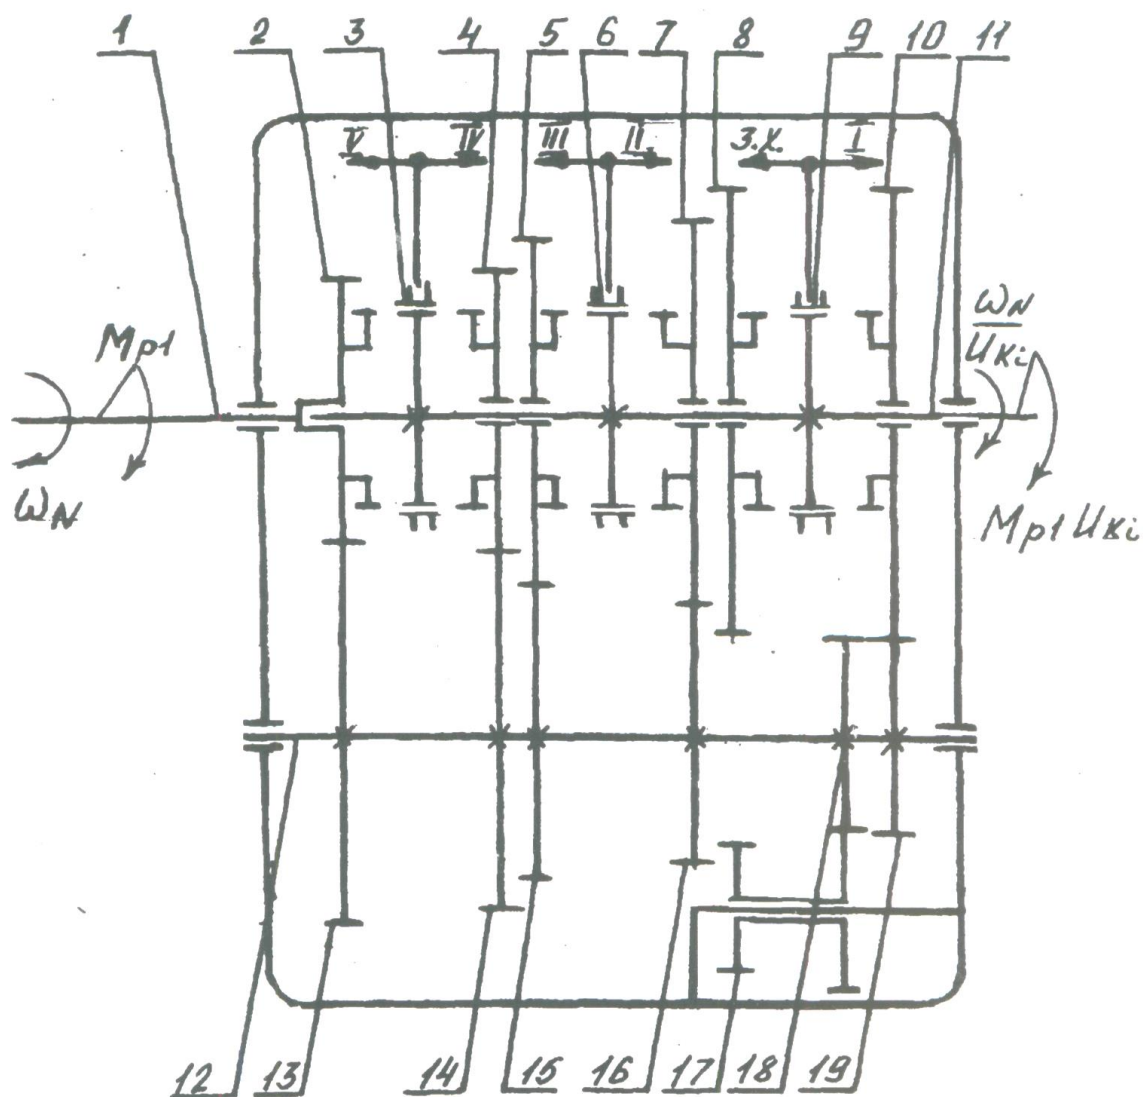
Кинематическая схема трёхвальной пятиступенчатой коробки передач
